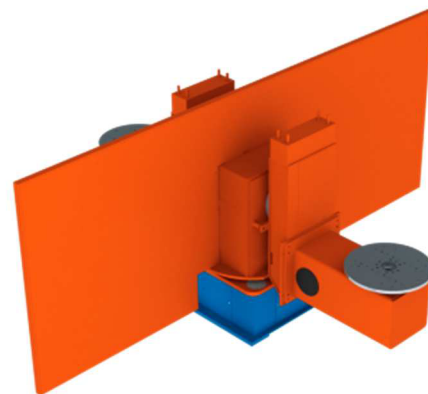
Robotizovaná obsluha více strojů jedním robotem [34]
